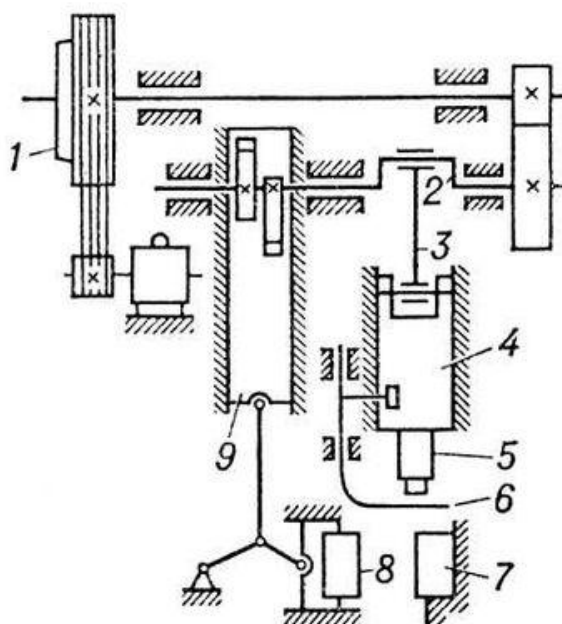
Кинематическая схема ГКМ: 1 - привод; 2 - кривошипный вал; 3 - шатун; 4 - главный ползун; 5 - пуансон; 6 - упор; 7 - неподвижная матрица; 8 - подвижная матрица; 9 - боковой ползун.
